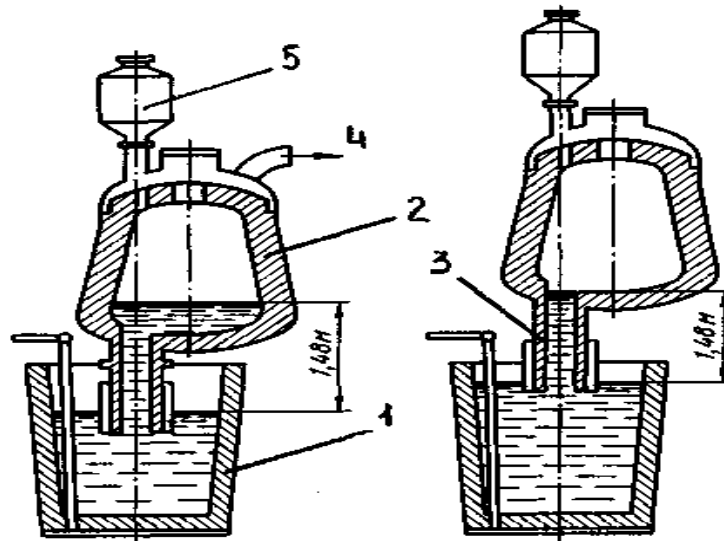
Камера для вакуумної обробки сталі в ковші
